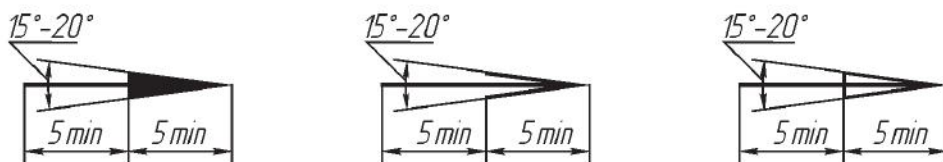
Форма и размеры стрелок, указывающих направление взгляда
